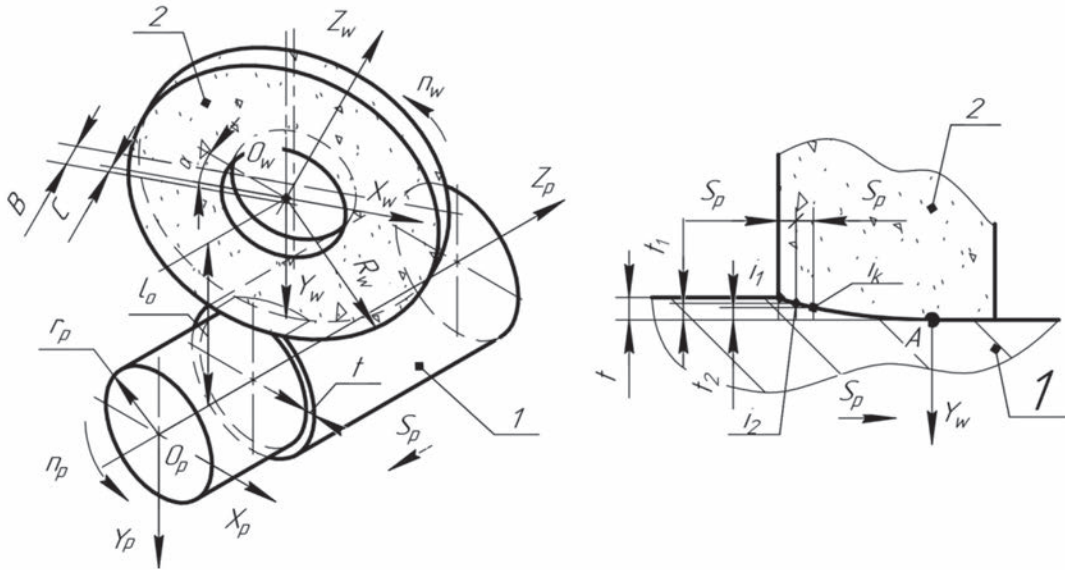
Шліфування циліндричного вала периферією орієнтованого інструмента
